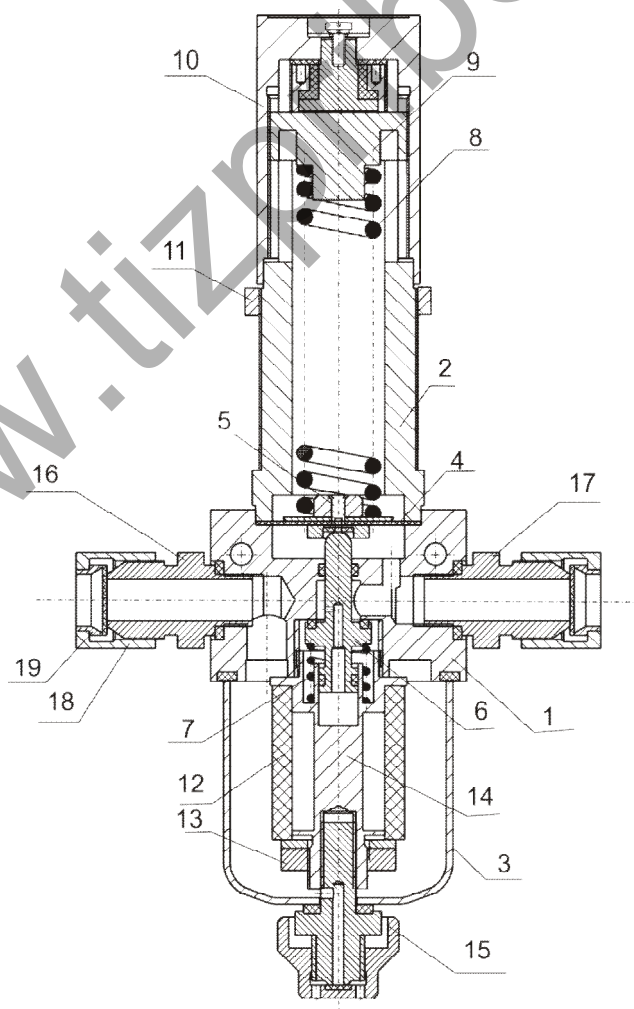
Конструкция редуктора РДФ-6/10
